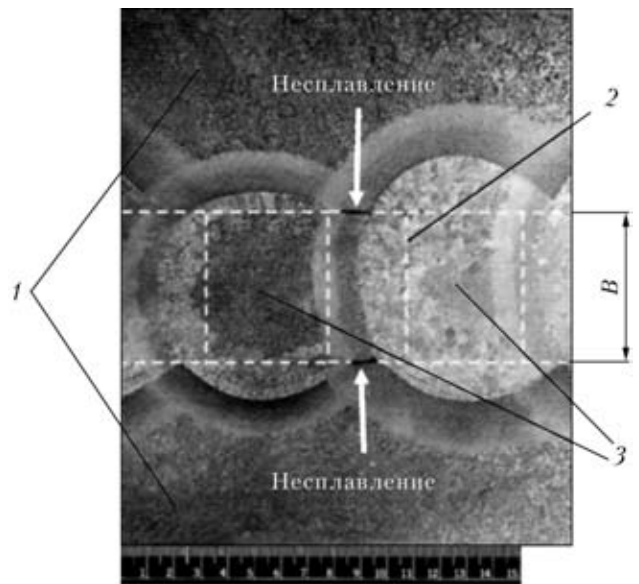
Поперечный макрошлиф фрагмента многослойного электрошлакового шва с дефектами: 1 — свариваемые детали; 2 — формирующая пластина-проставка; 3 — слой шва
